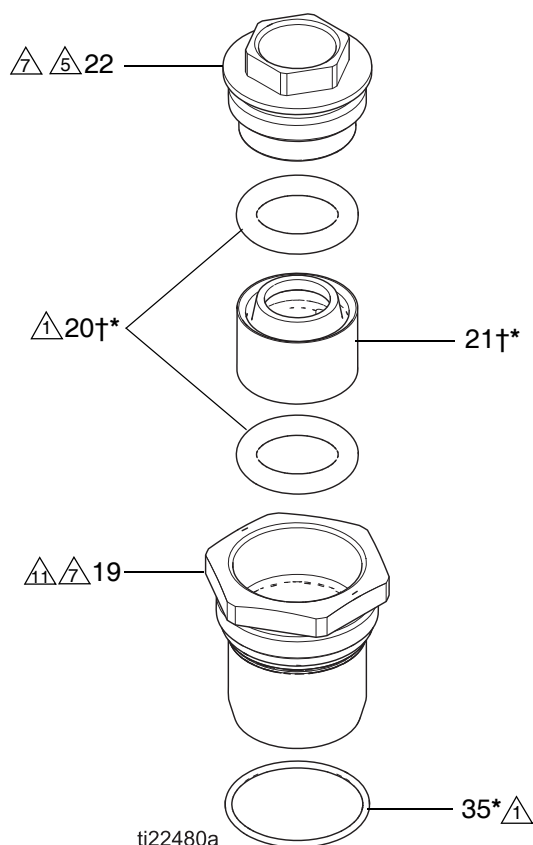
Démontage ou montage de la cartouche de presse-étoupe
